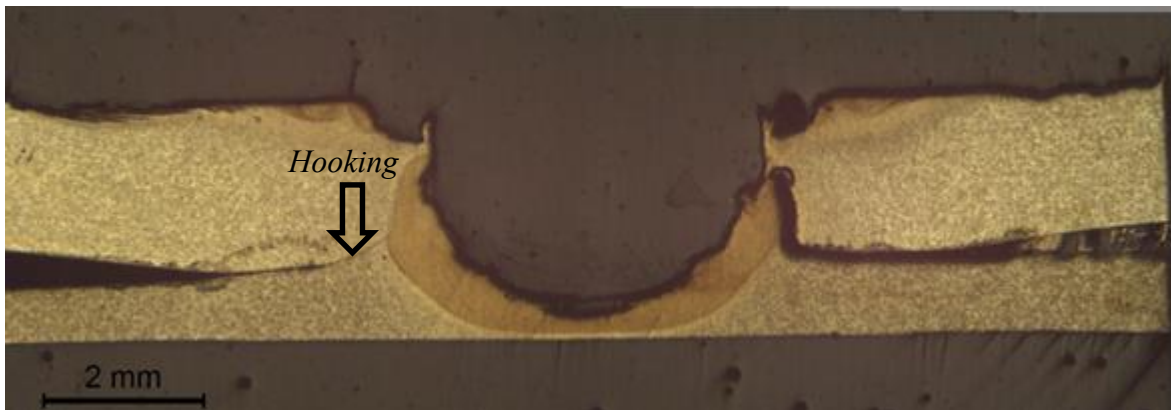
Macrografia do provete soldado W-1.6.
